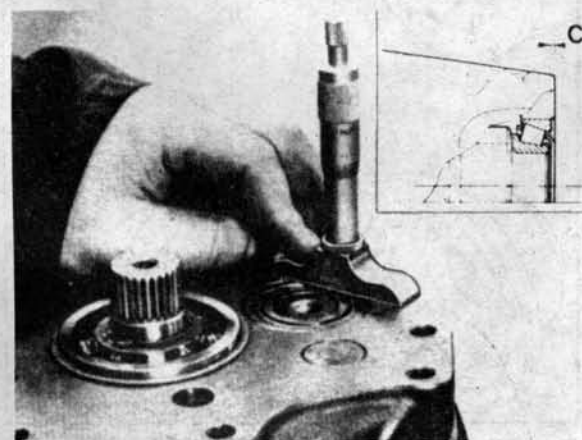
Подбор дистанционных прокладок подшипника промежуточного вала в КПП типа М45R
